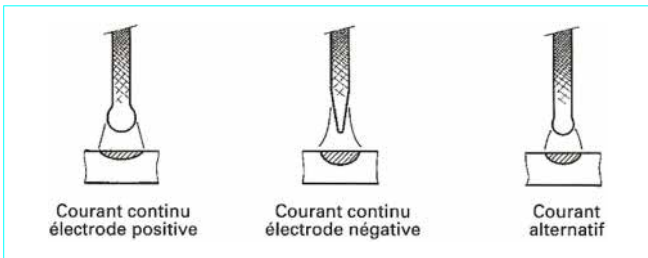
Formes des électrodes pour soudage TIG
